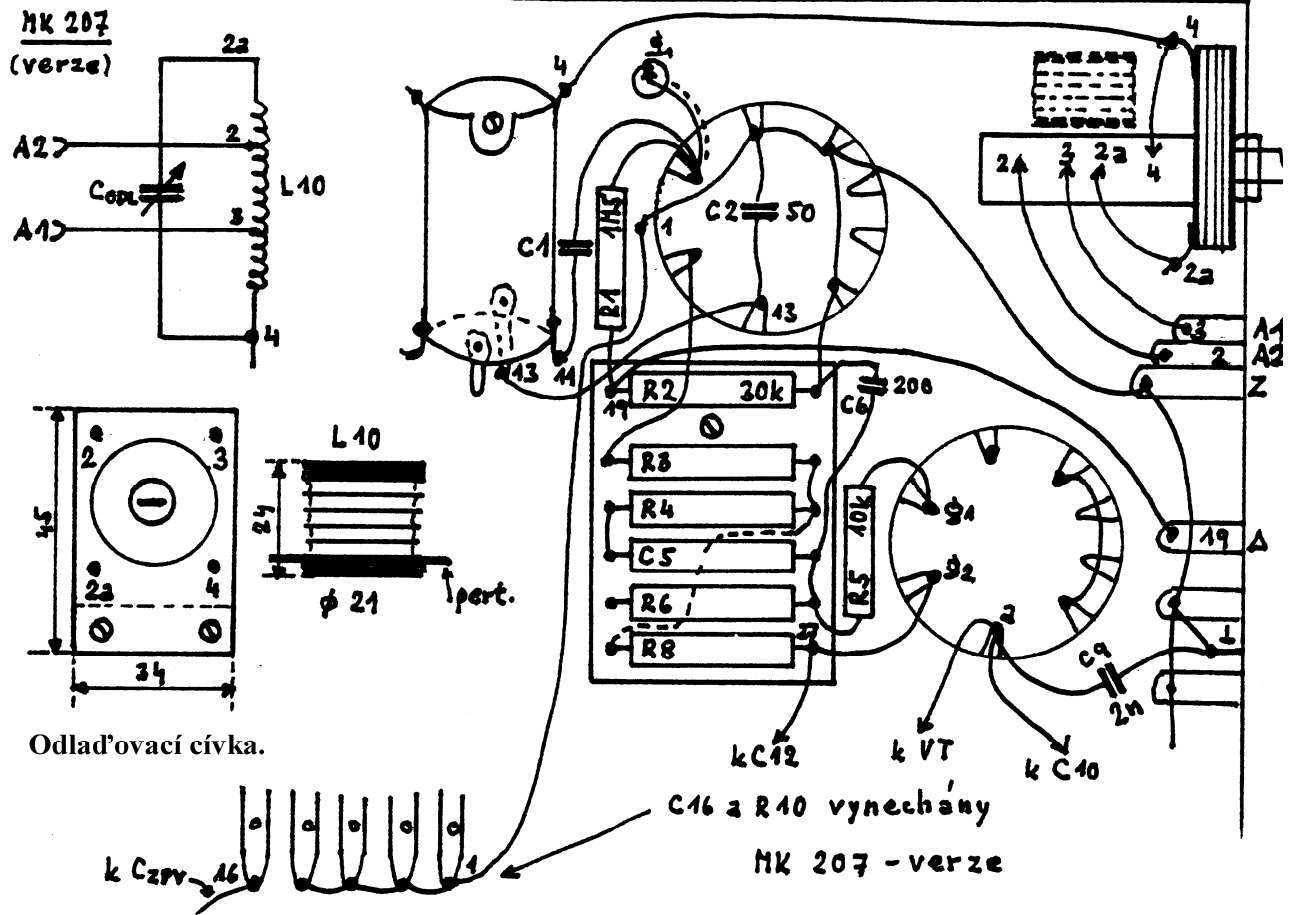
Rozmístění součástek a vedení spojů pod šasi.
